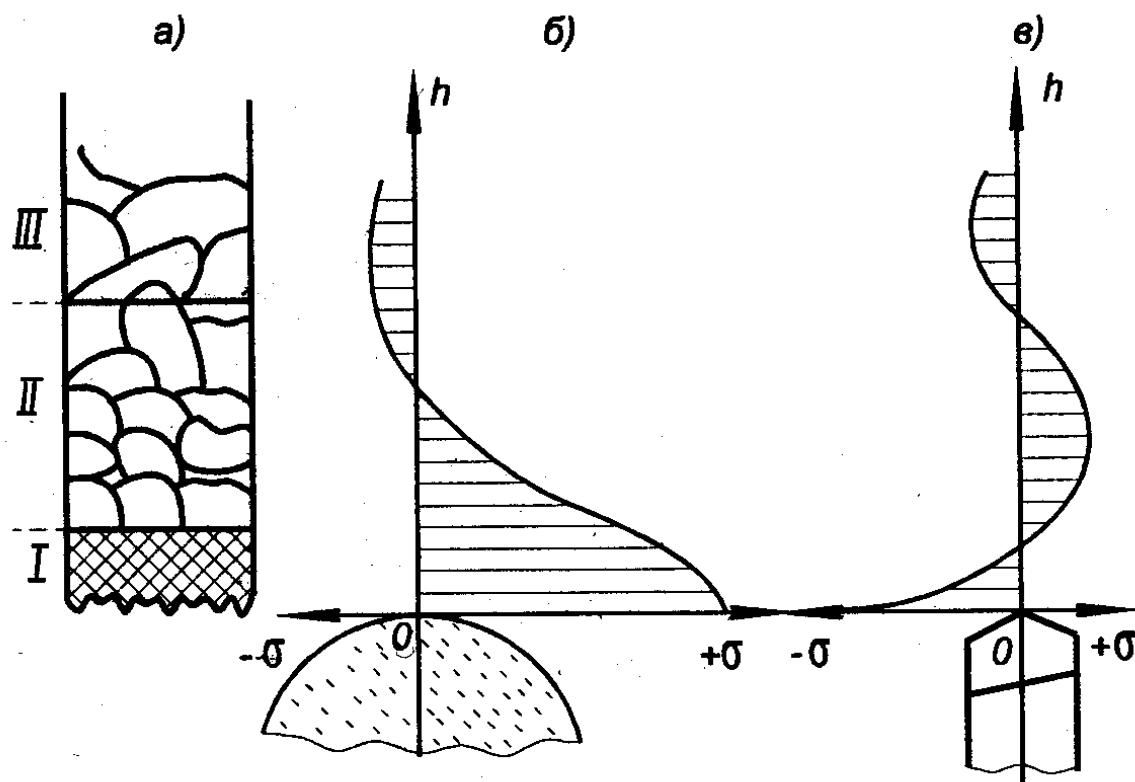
Поверхностный слой детали из стали: а) – структура; б) – напряжения в поверхностном слое после абразивной обработки; в) – напряжения в поверхностном слое после лезвийной обработки
